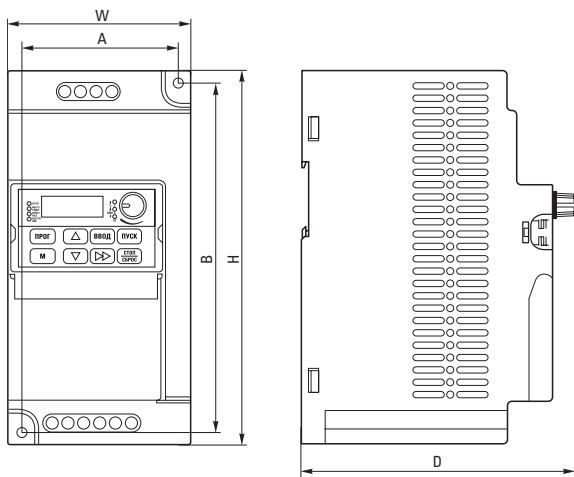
Внешний вид пластмассовой конструкции и монтажные размеры VECTOR-80
